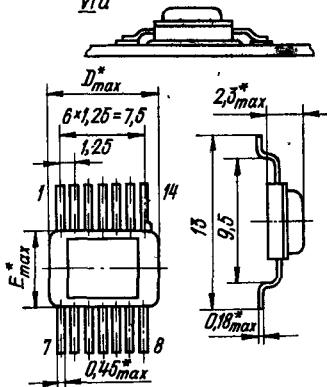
Габаритные и установочные размеры и варианты установки микросхем в корпусе типа 3 (* обозначены размеры для справок)
